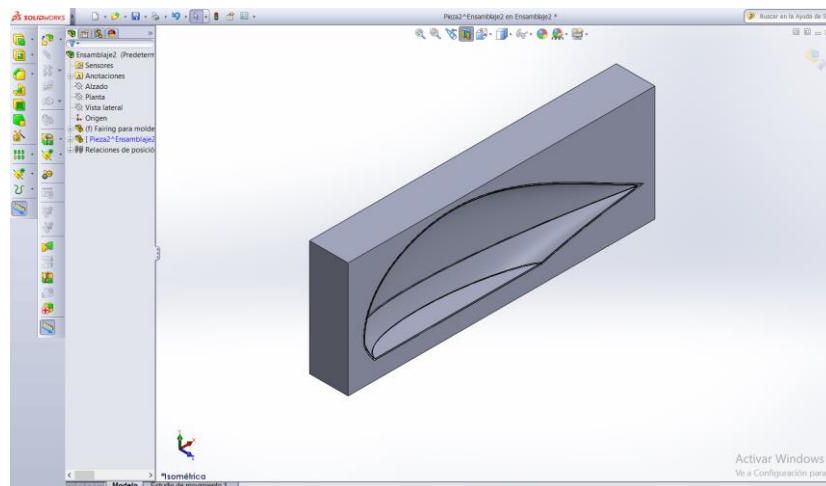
Molde cavidad del carenado avión Diamond DA20
